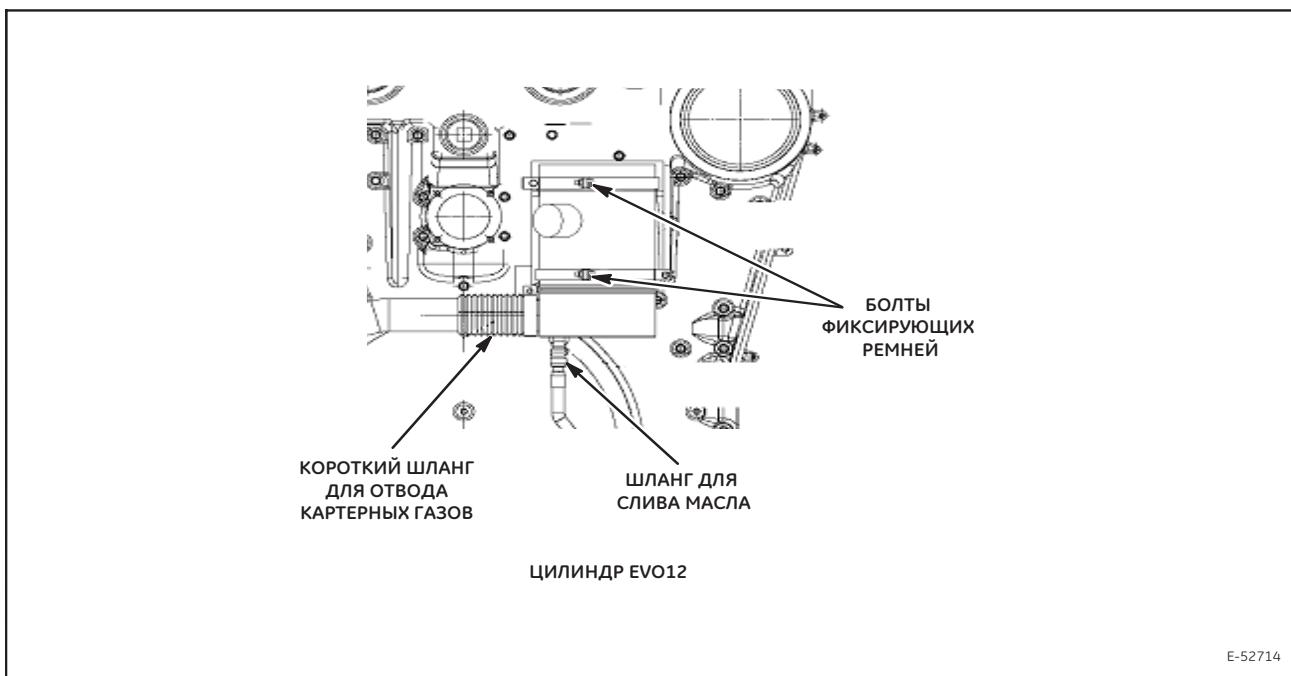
Крепление коагулятора к переднему концу двигателя (типичное)
